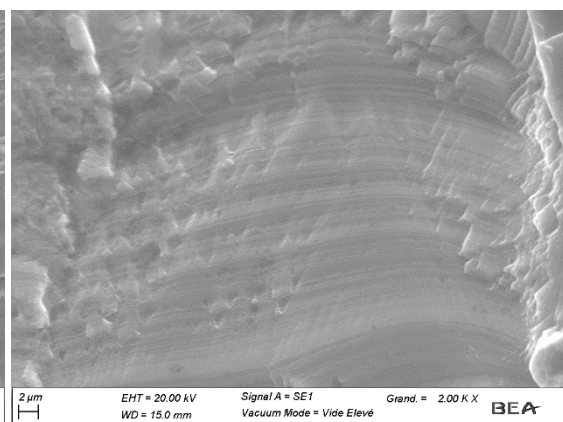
vue d'ensemble de la zone de rupture A (Source : BEA)
